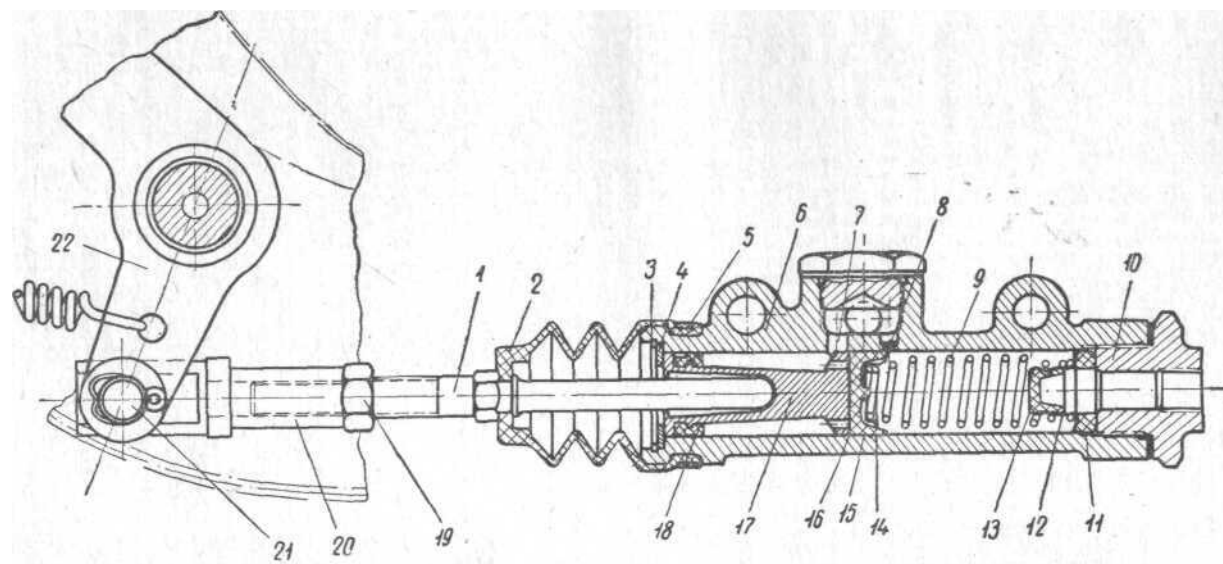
Главный тормозной цилиндр автомобиля модели 407:
